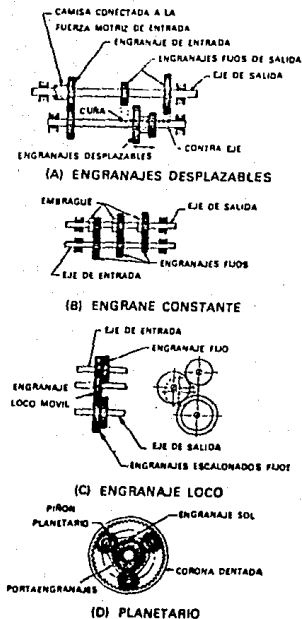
TRANSMISION REGULABLE DE ENGRANAJES
